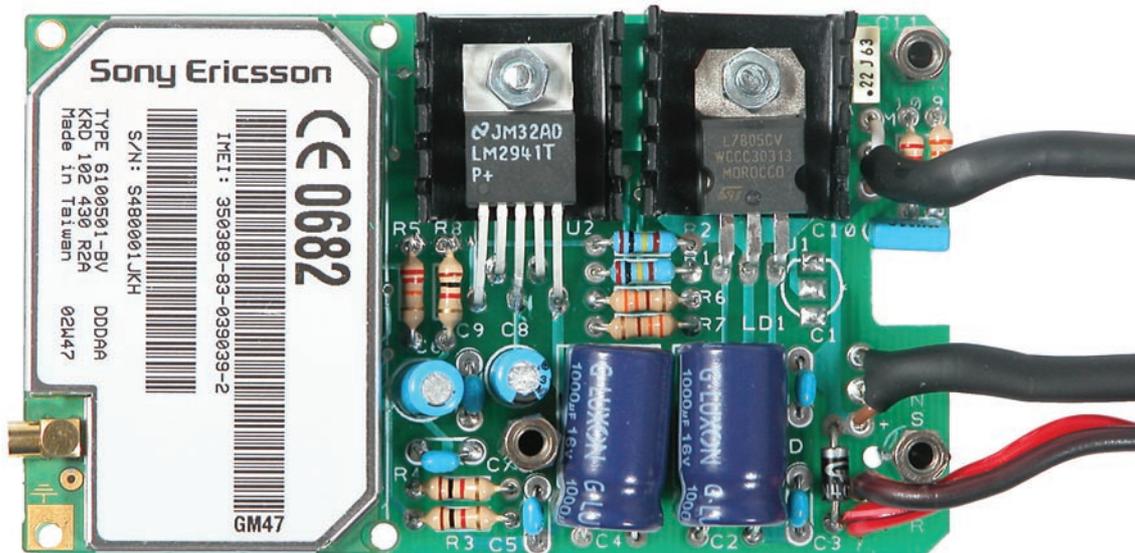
Photo d'un des prototypes de la platine du système d'écoute vue du côté composants.
